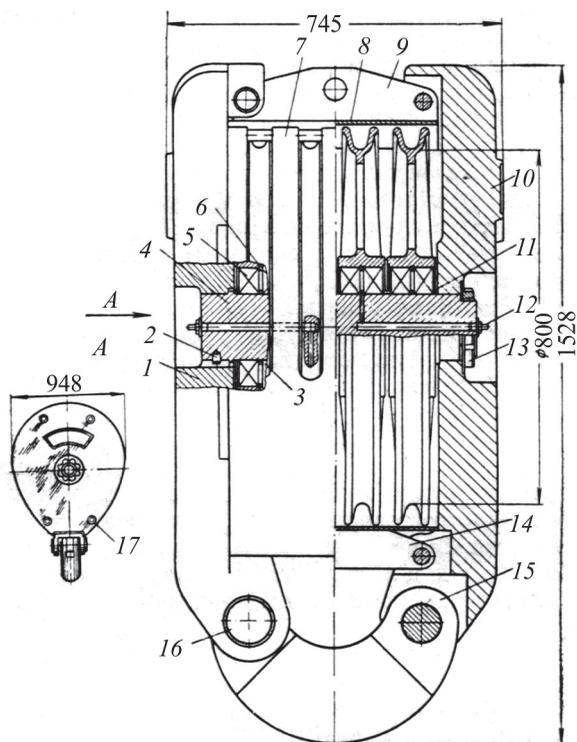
Талевый блок: 1, 10 – щеки; 2 – штифт; 3, 6, 11 – кольца; 4 – ось; 5 – роликоподшипники; 7 – откидные кожухи; 8 – канатный блок; 9 – верхний щит; 12 – масленки; 13 – гайка; 14 – нижний щит; 15 – серьга; 16 – палец; 17 – болт
